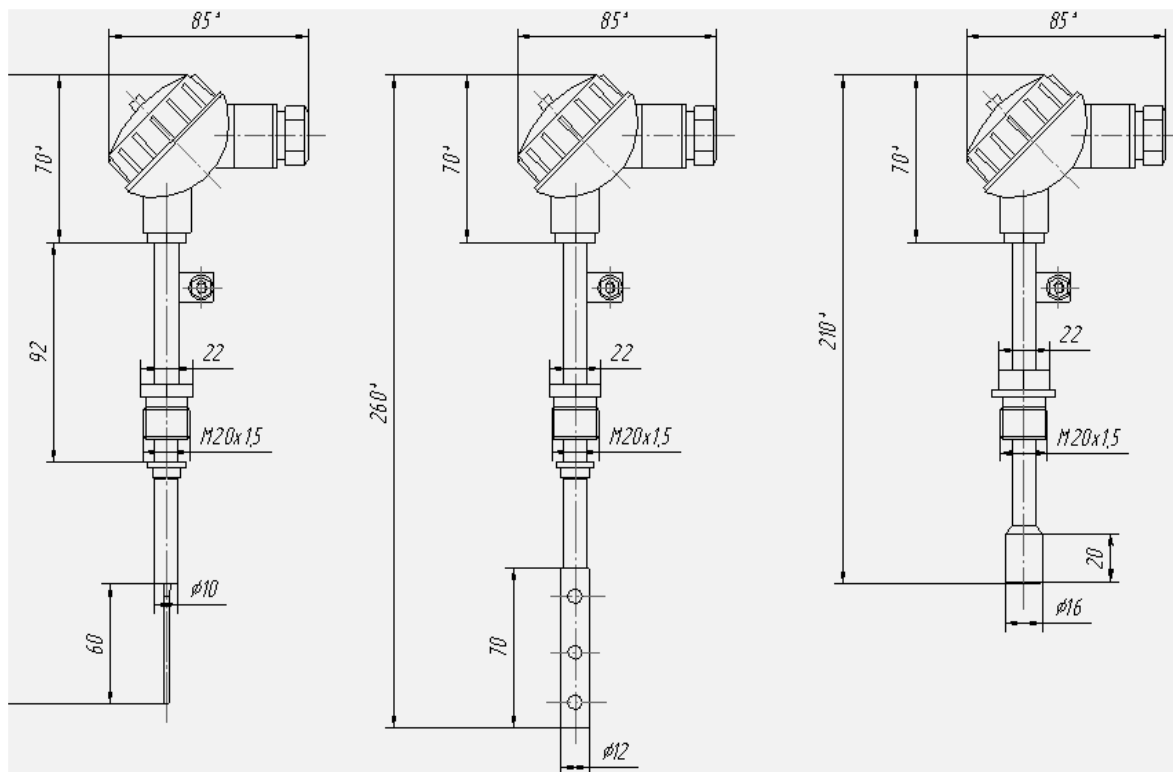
Внешний вид и габаритные размеры сигнализатора СЖУ-1-Э:
